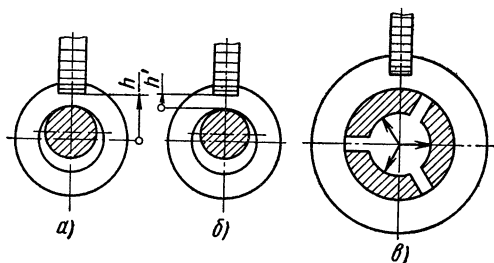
Схемы для определения погрешности установки деталей по внутренней цилиндрической поверхности
